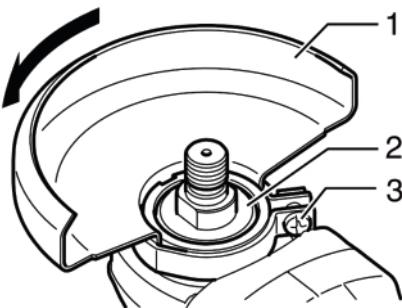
Установка/снятие защитного кожуха аккумуляторной угловой шлифовальной машине серии DLAG.
